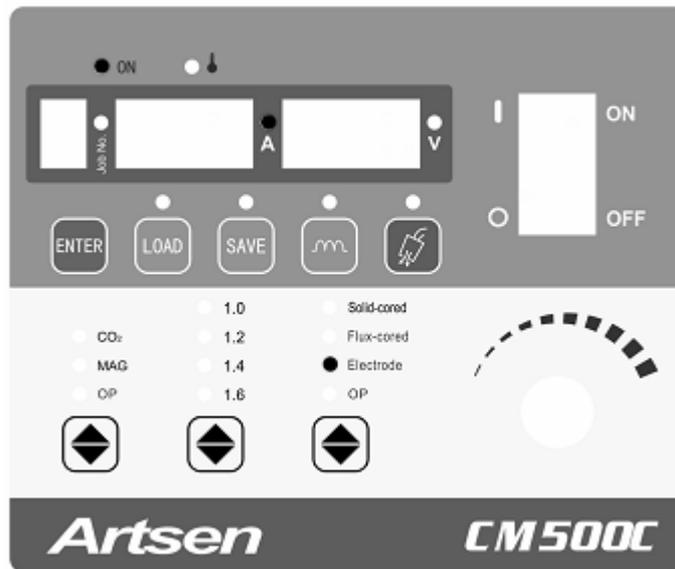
Выбор режима ручной дуговой сварки штучным электродом
